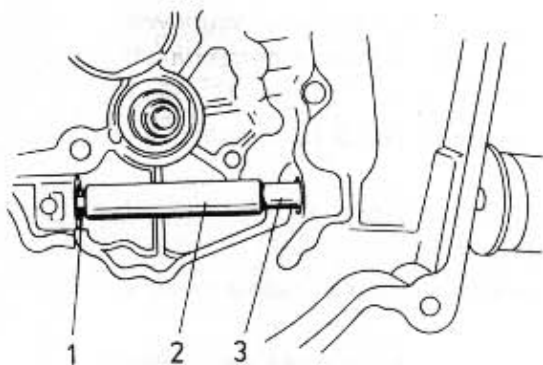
DEMONTAŻ WEWNĘTRZNEJ TULEJKI ŁOŻYSKUJĄCEJ WAŁEK WYŁĄCZAJĄCY SPRZĘGŁO
